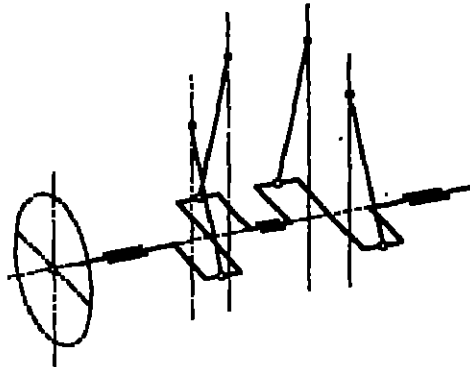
Kurbelwellen der Vierzylindermaschine.
